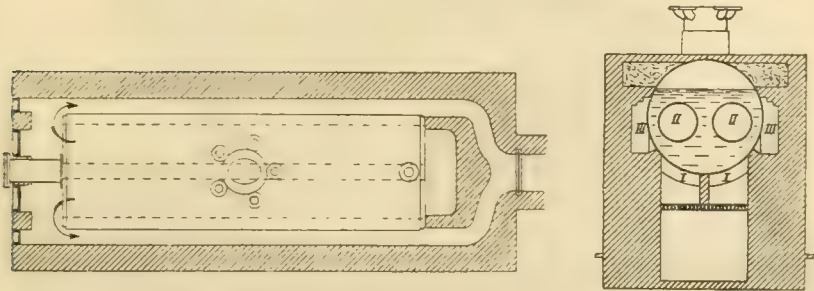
Grundriss zu Fig. 151. *a* Wasserstandsstutzen, *b* Reinigungsstutzen, *c* Dampfdorn.
